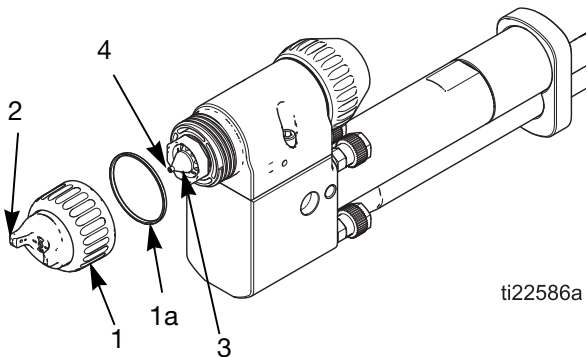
Limpieza del cabezal de aire y de la boquilla de fluido
